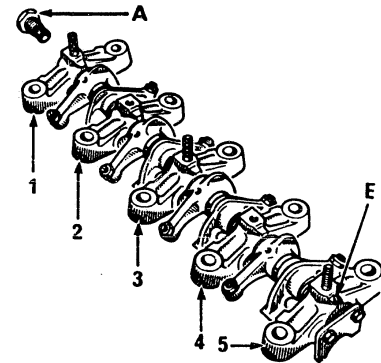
Motoren J6R und J7T: Die Welle mit den Kipphebeln kann nach dem Lösen der Zylinderkopfschrauben abgehoben werden, ohne dass der Zylinderkopf ausgebaut wird. Falls die Bohrung E noch nicht mit einem «vollen» Stift verschlossen ist, ist dies nachzuholen.
